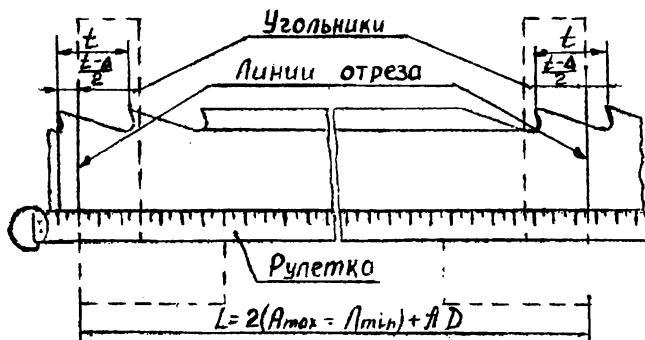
Разметка полотна ленточной пилы для сварки
